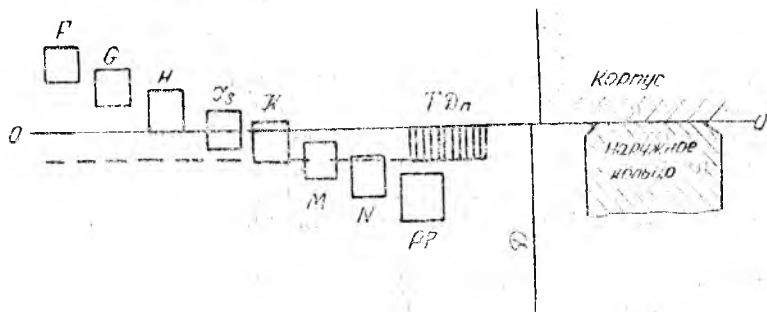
Соединение наружного кольца подшипника качения с корпусом
